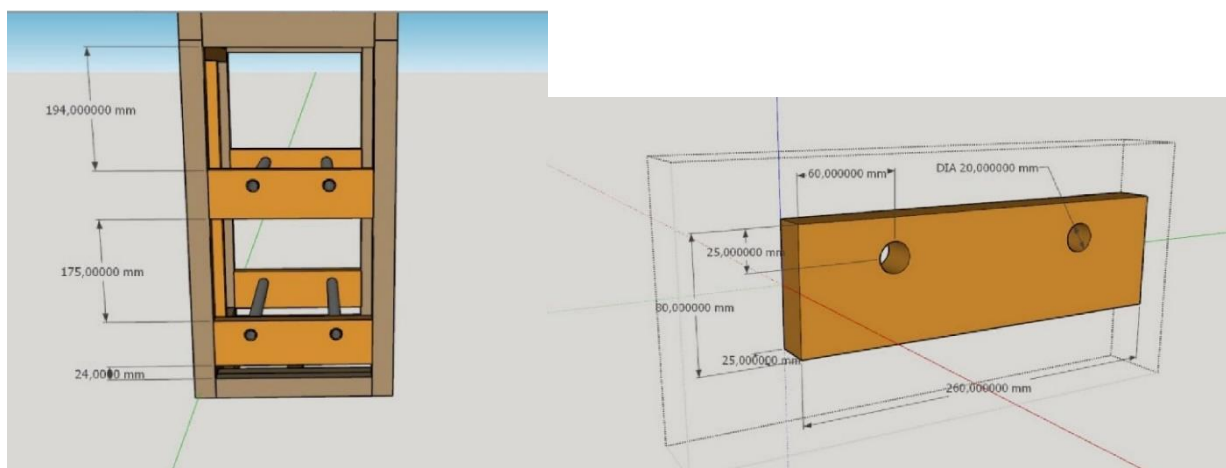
Бруски для кріплення алюмінієвих трубок
